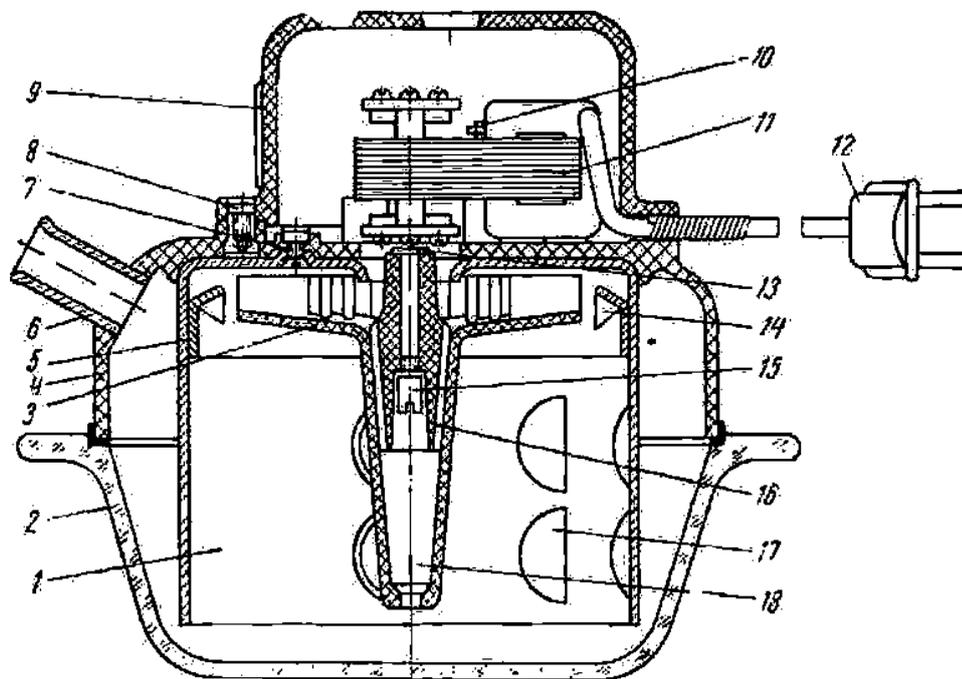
Ионизатор И5-5А; 1 - аппарат; 2 - сосуд для воды; 3 - крыльчатка; 4 - пластмассовый корпус аппарата; 5 - алюминиевый корпус распылителя; 6 - выходной патрубок распылителя; 7, 8, 9 - винты; 10 - пластмассовый кожух двигателя; 11- асинхронный двигатель; 12 - соединительный шнур; 13 - втулка; 14 - зубчатый венец; 15 - гайка; 16 - конусная втулка; 17- жалюзи; 18- внутренняя полость конуса крыльчатки
